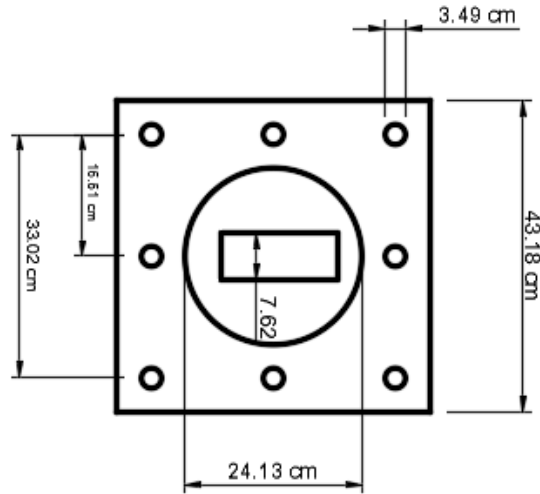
Dimensiones de placa disipador 330 KIP (Fuente propia)
